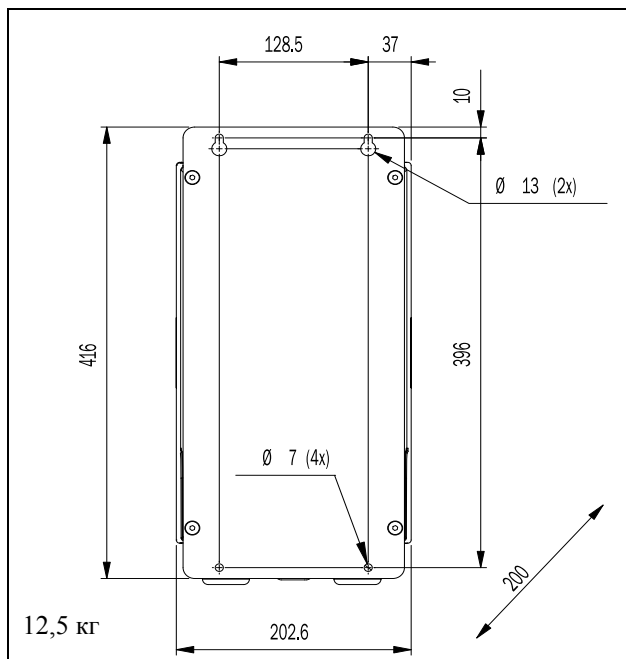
Устройство Emotron FDU моделей 48/52-003 – 018 (Типоразмер корпуса B)
